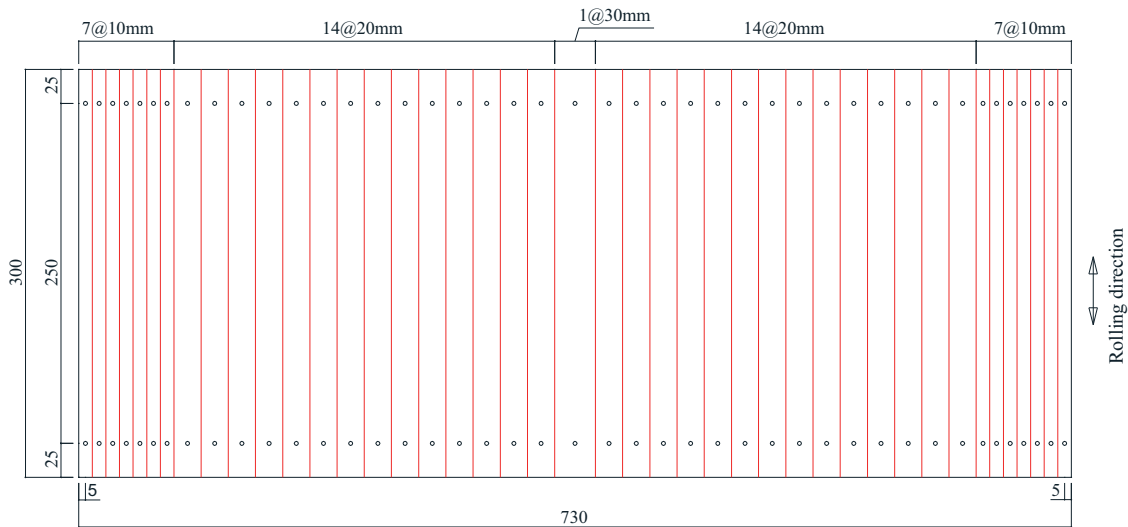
Vue en plan d'un spécimen de type oxycoupage de type T1 (en mm).
